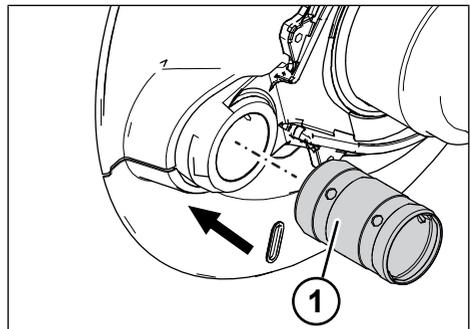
Colocar el casquillo del rodamiento de levas portapastillas
